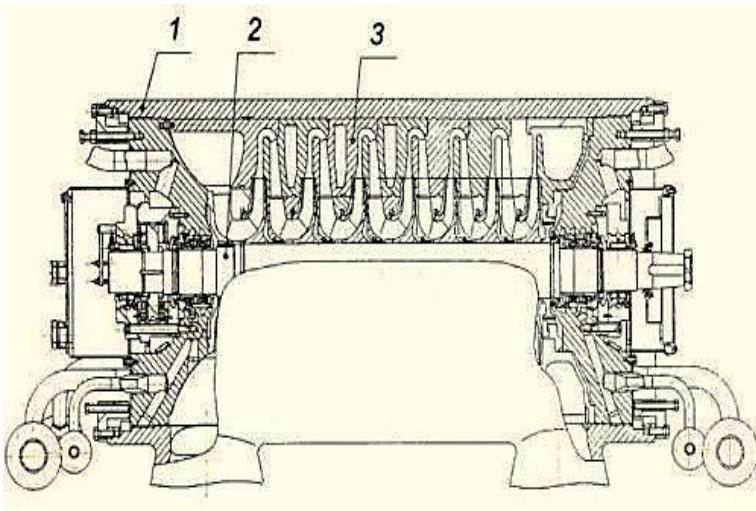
Базовий корпус із вертикальним рознімом
